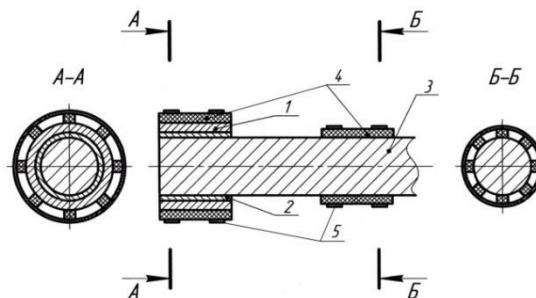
Конструкция подшипникового узла скольжения: 1 – корпус подшипника скольжения; 2 – кольцевой вкладыш из немагнитных материалов; 3 – вал; 4 – постоянные магниты; 5 – хомуты
